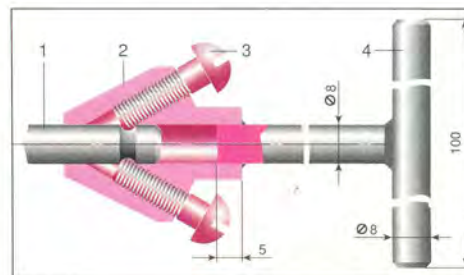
Приспособление с винтовым зажимом стержня: 1 – стержень клапана; 2 – корпус; 3 – зажимные винты (3 шт.); 4 – рукоятка.
